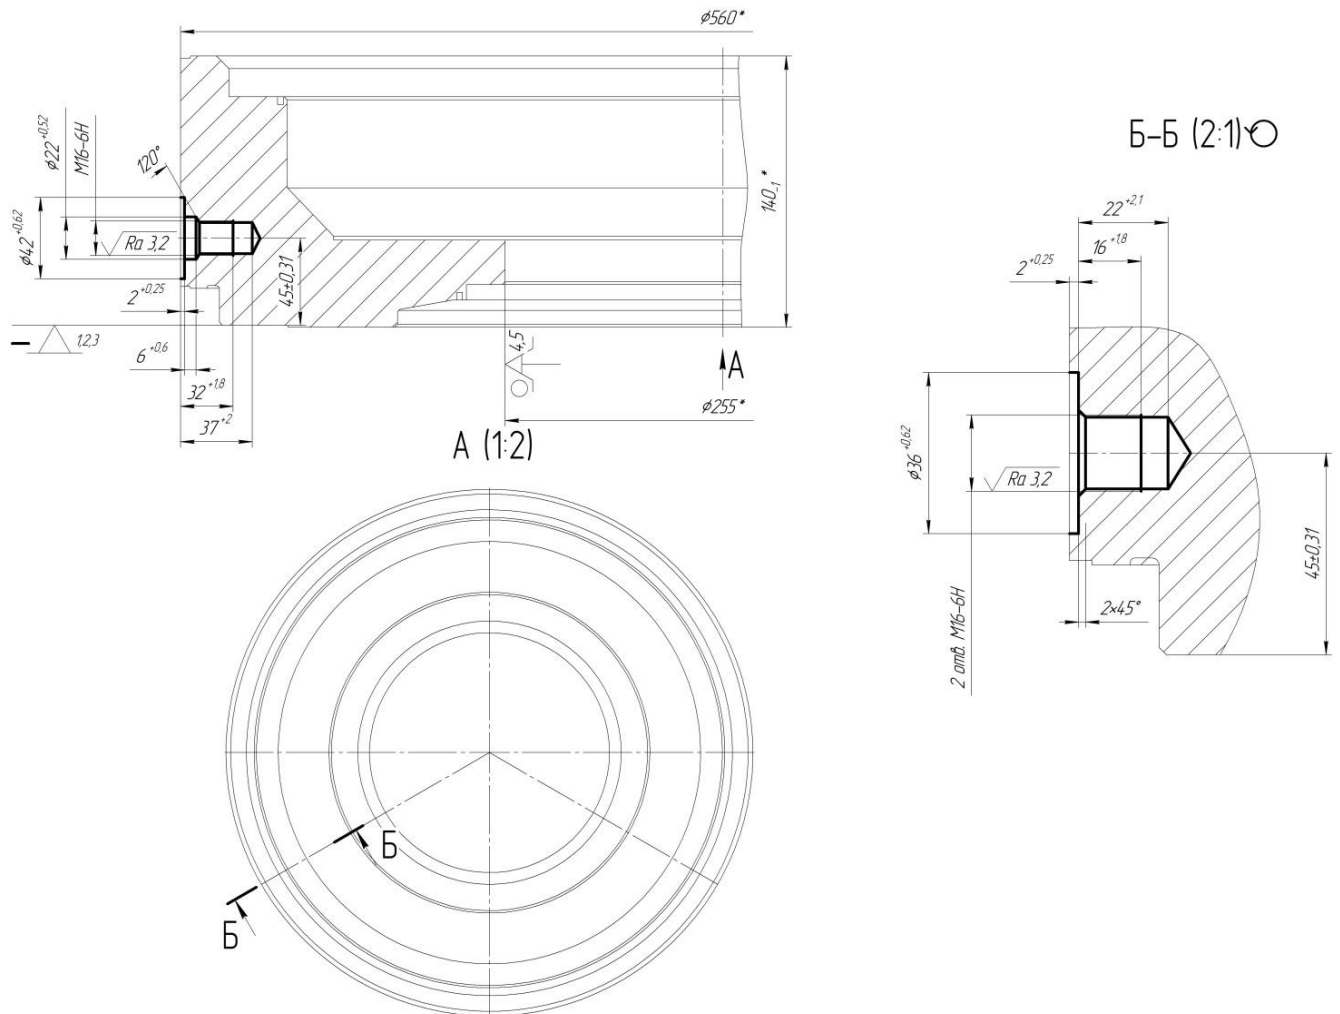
Схема базування заготовки на комплексній операції (другий варіант)
